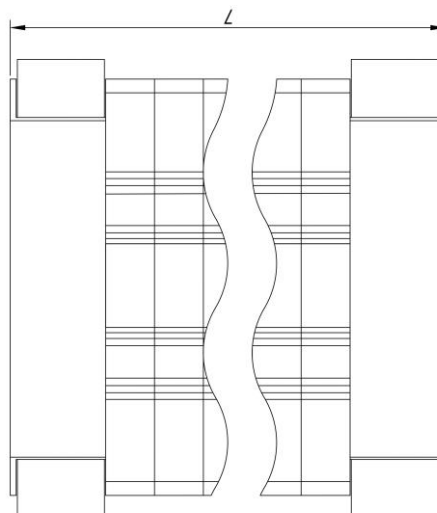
Общий вид рабочей крышки ЭПК. Вид спереди.
